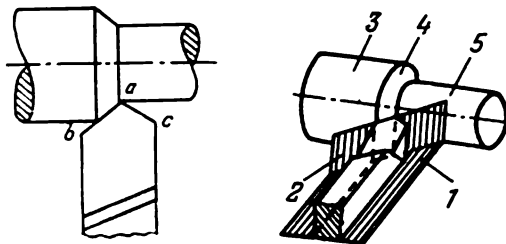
Surfaces principales de la pièce à usiner et les plans de départ
